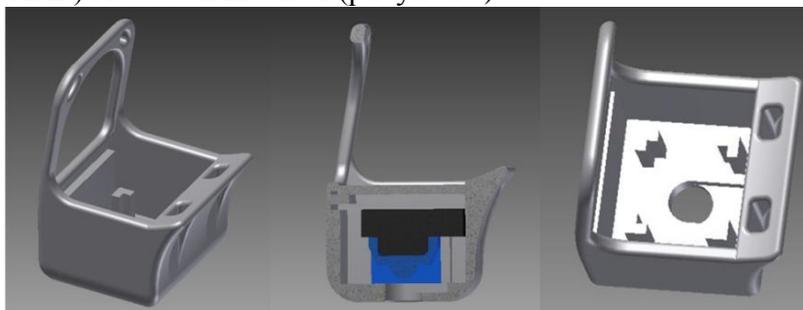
Сборка корпуса в САПР Autodesk Inventor
